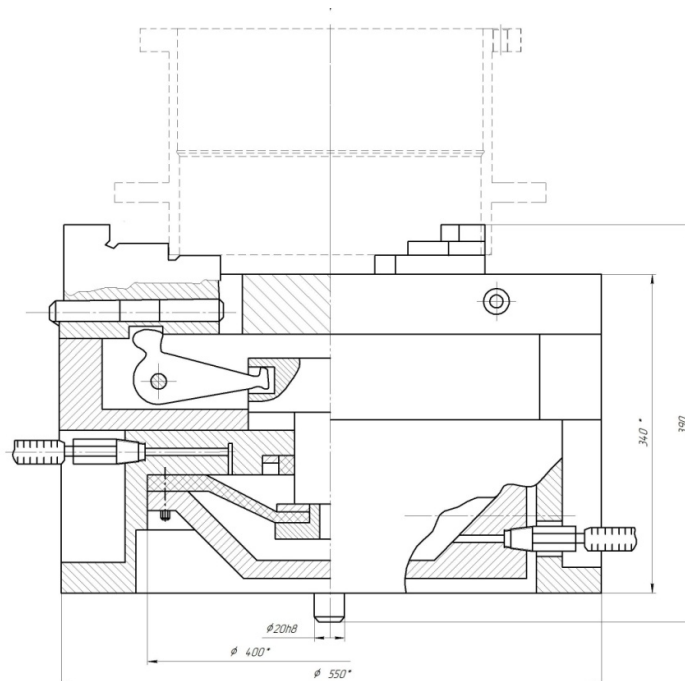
Пристрій для закріплення деталей при свердлуванні
